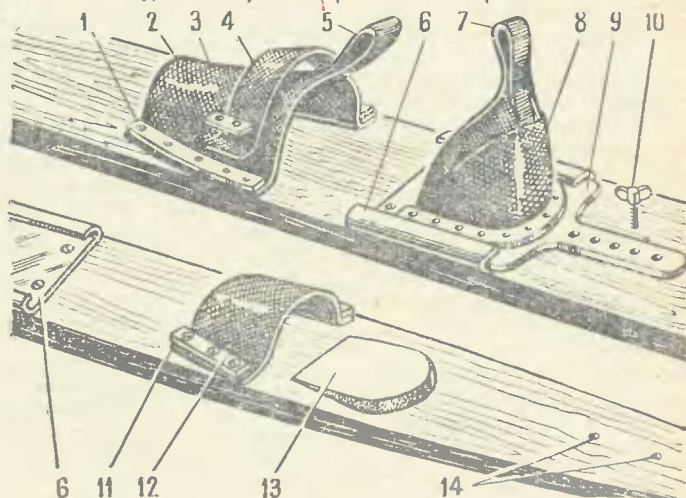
Крепление любительской конструкции с регулируемой по размеру ноги пяткой: 1 — планка, прижимающая носочную резинку, 2 — носочная резинка, 3 — дополнительная планка, 4 — перемычка носочной резинки, 5 — ушко носочной резинки, 6 — салазки пятки, 7 — ушко пятки, 8 — пятка, 9 — основание пятки, 10 — фиксирующий болт, 11 — планка, прижимающая заднее крепление, 12 — резинка заднего крепления, 13 — клиновидная подкладка под пятку, 14 — болты, крепящие киль.
